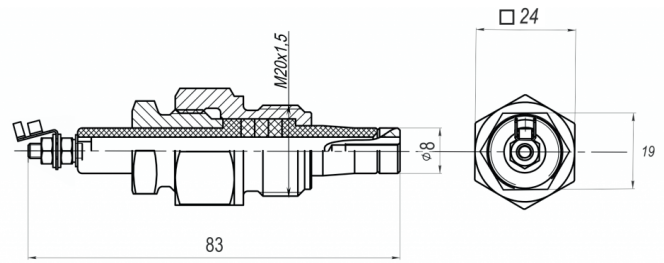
габаритные и установочные размеры датчика КДУ-1
